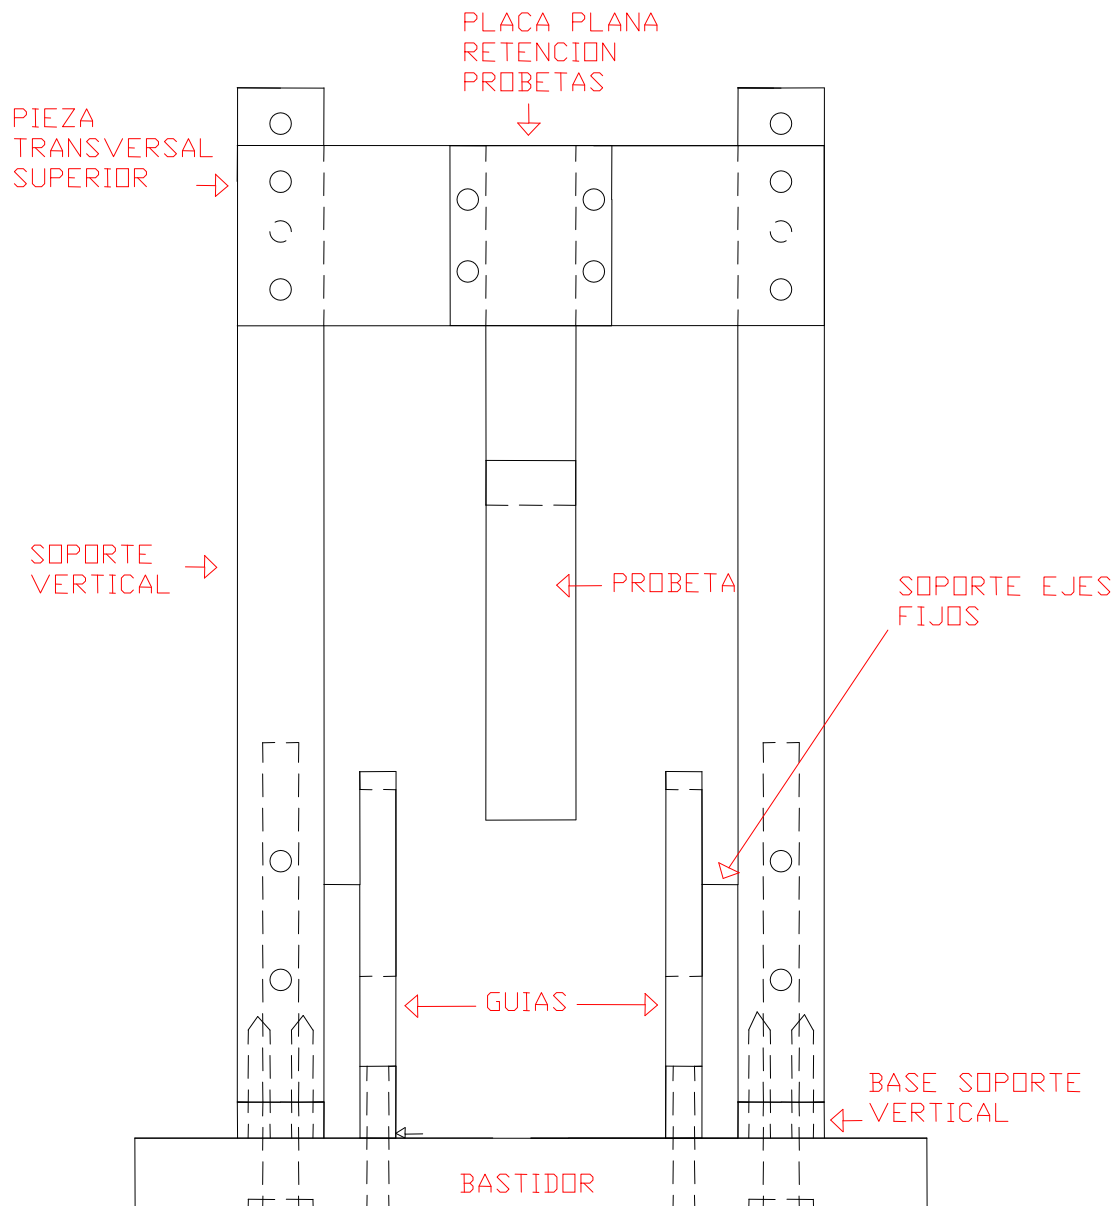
Vista frontal conjunto sin soporte móvil.
